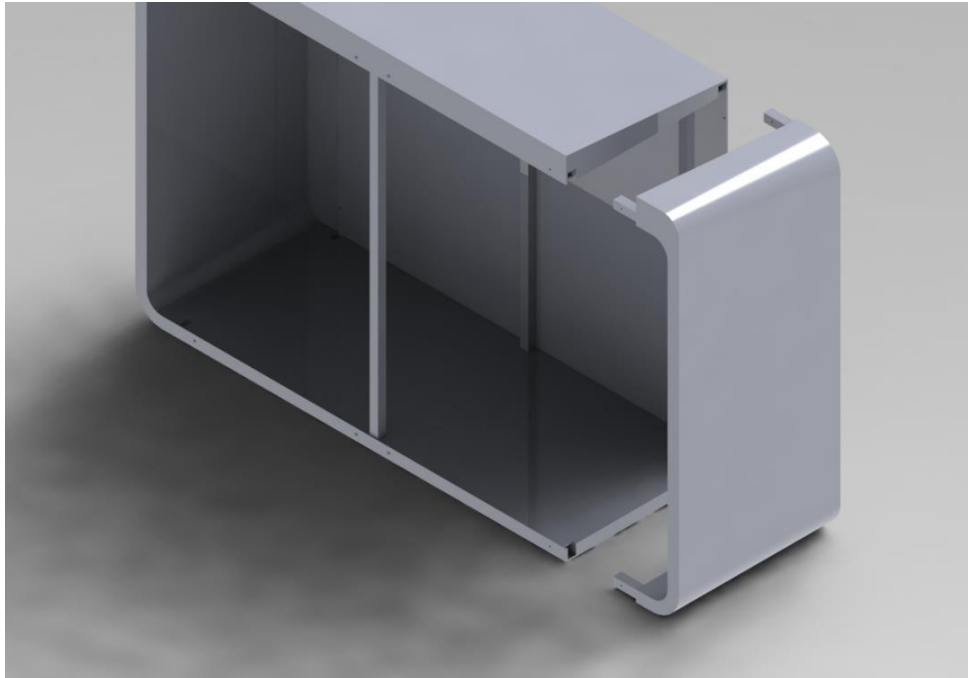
Ensamblaje subconjunto 1. Unión 1.2 - 1.3, 1.4.
